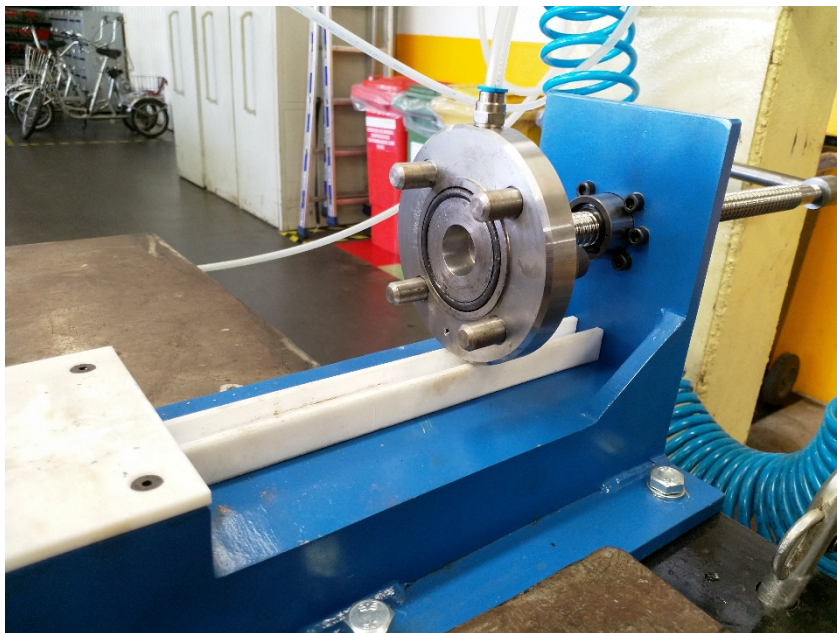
Equipamento de teste já fabricado – vista nº2.
